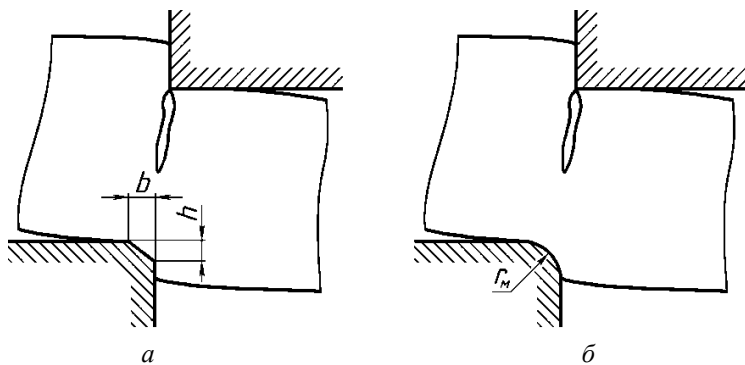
Чистовая вырубка и пробивка путем заваливания (а) или закругления (б) одной из режущих кромок
